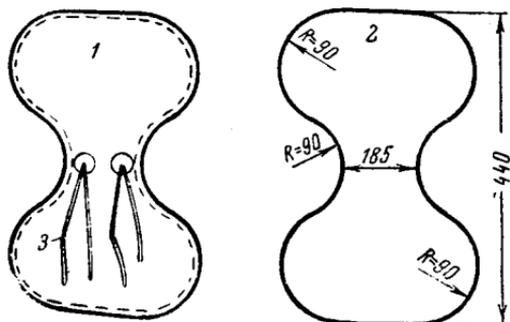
Потники для горбатой седелки: 1 — покрывка; 2 — пласт войлока; 3 — сыромятная шивка для прикрепления потника
